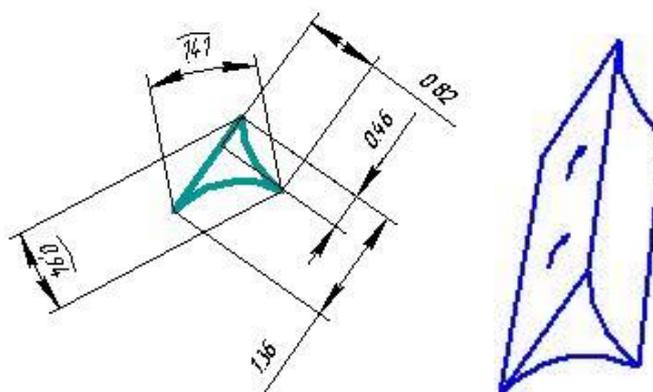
Размеры профиля (в метрах) и вид герметизирующей вставки
